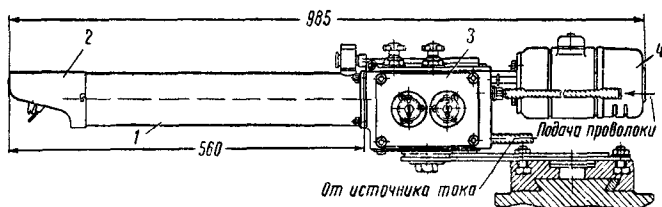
Универсальный трехфазный металлизатор УТМ-1:
